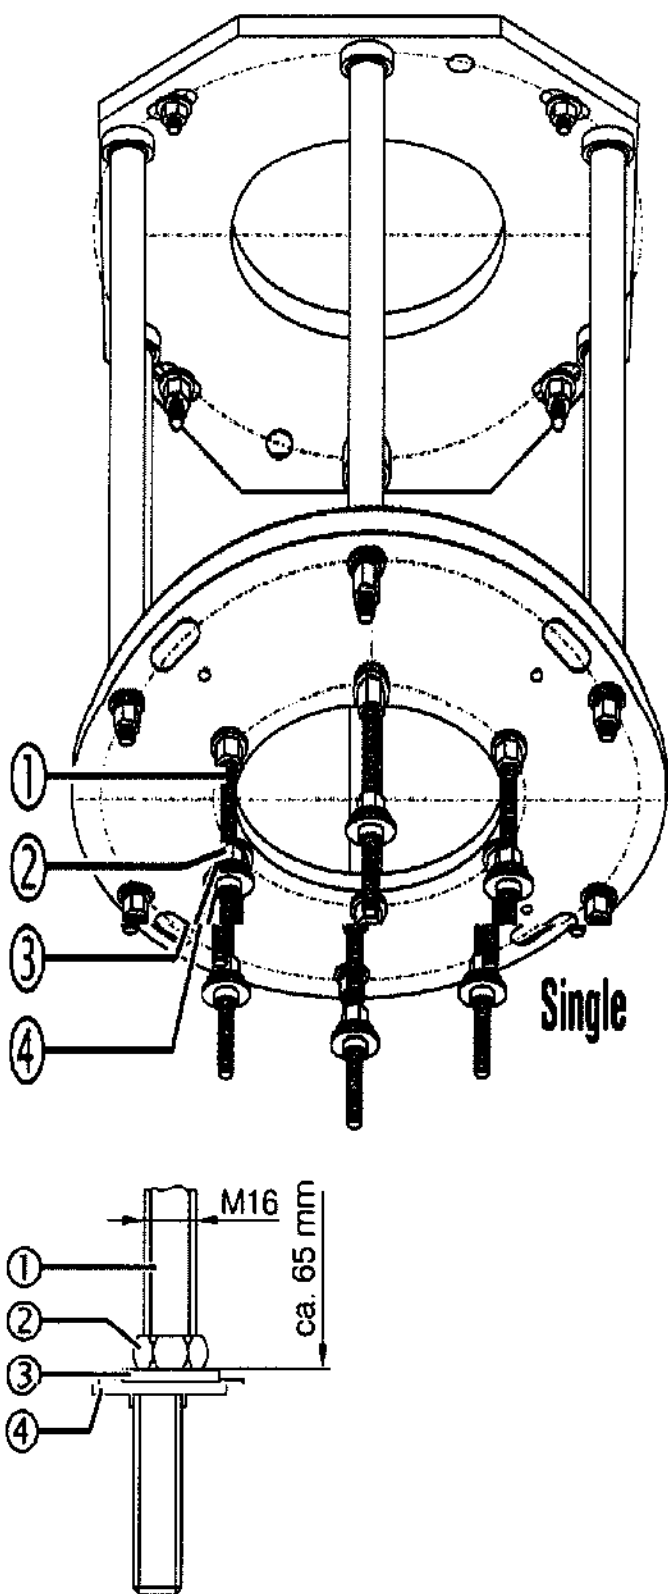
Установка шестигранной гайки (Одинарной и двойной)
